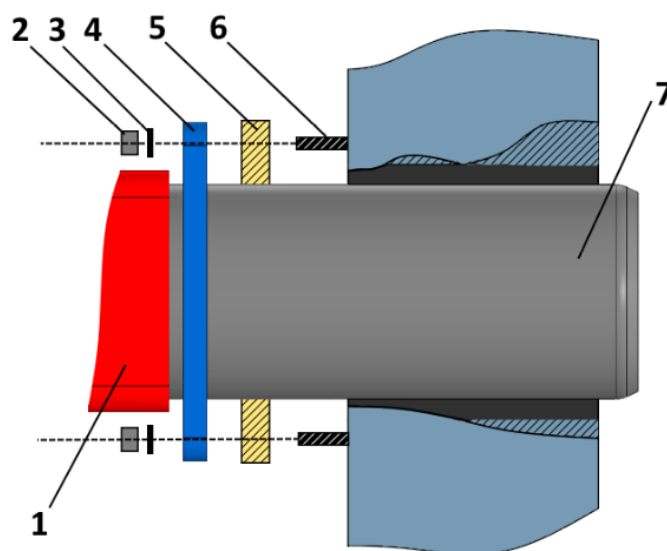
Пример монтажа горелки ЕММА-СО.2-ЛО к топке. 1 – Горелка; 2 – Крепежная гайка; 3 – Шайба; 4 – Монтажный фланец; 5 – Теплоизоляционный уплотнитель; 6 – Шпилька; 7 – Оголовок горелки.
